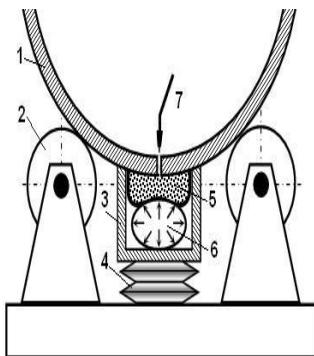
Флюсовая подушка для сварки продольных швов обечайки.
